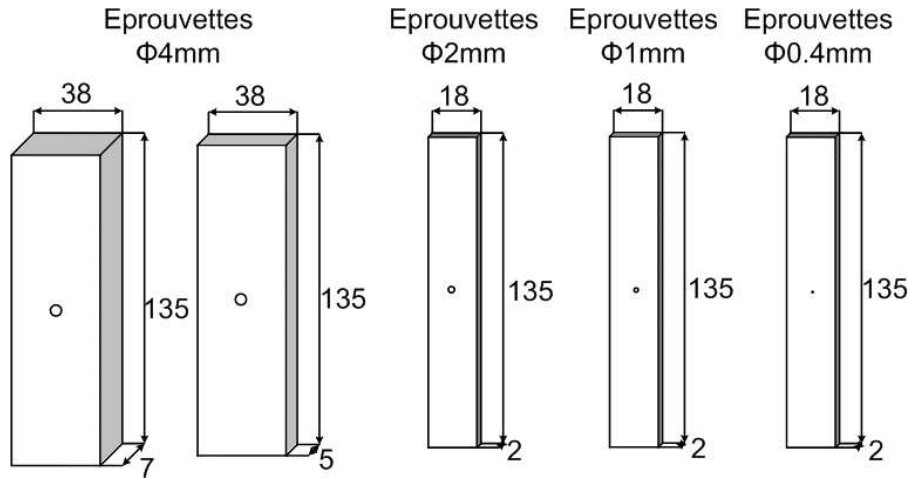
Géométrie des éprouvettes à un seul trou
